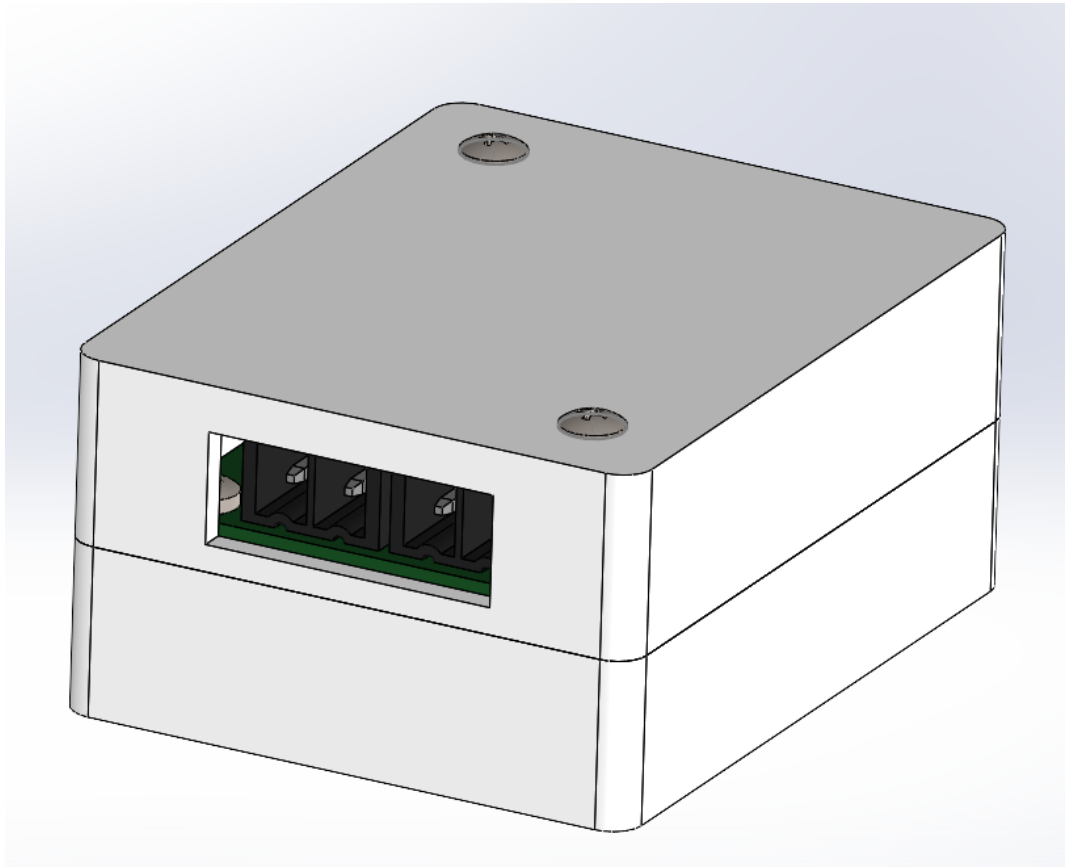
Зовнішній вигляд корпусу
